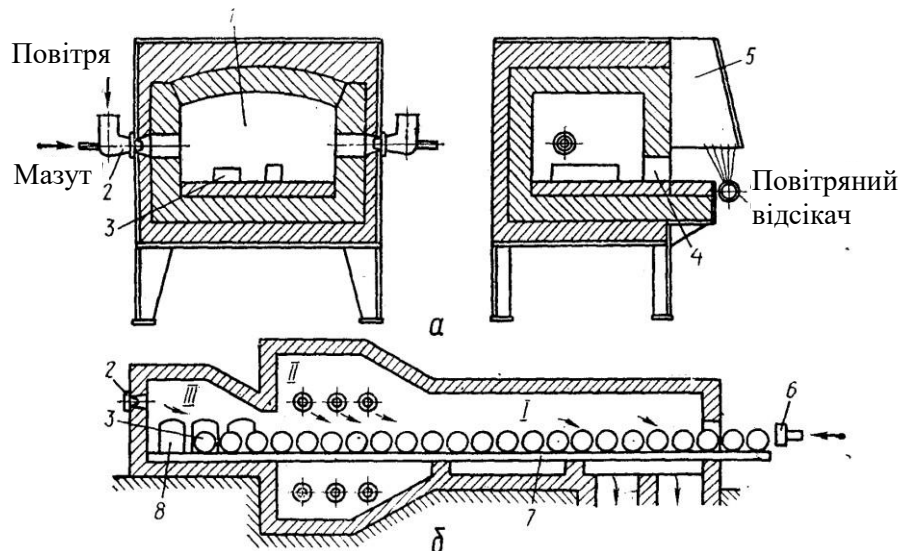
Полум'яні печі для нагрівання заготовок
